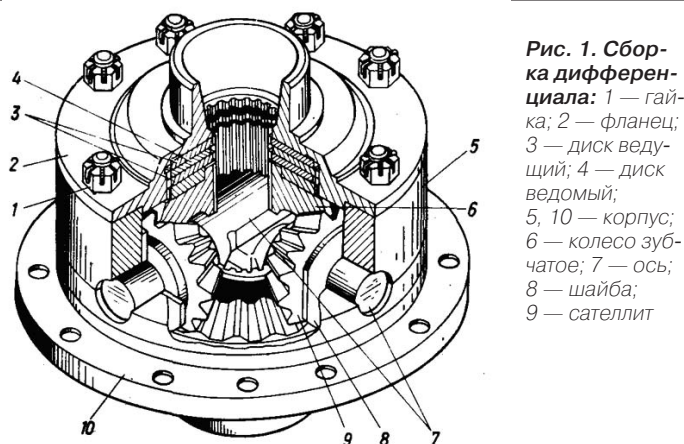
Сборка дифференциала: 1 — гайка; 2 — фланец; 3 — диск ведущий; 4 — диск ведомый; 5, 10 — корпус; 6 — колесо зубчатое; 7 — ось; 8 — шайба; 9 — сателлит
